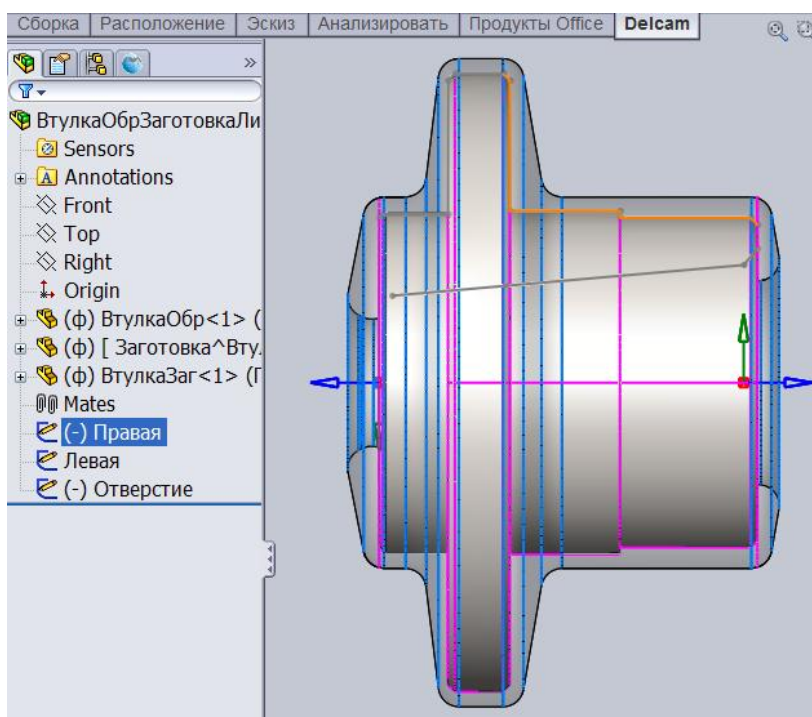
Створений вручну контур для обробки зовнішньої поверхні
